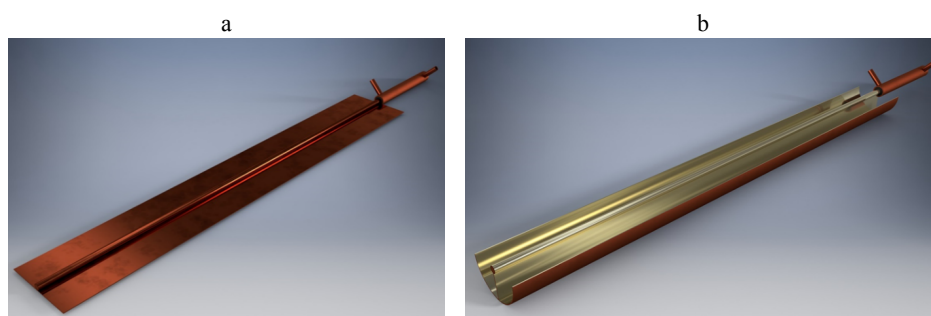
3D-модель конструкции солнечного коллектора на основе медного двухфазного термосифона с плоской (а) и цилиндрической (б) поглощающими панелями
